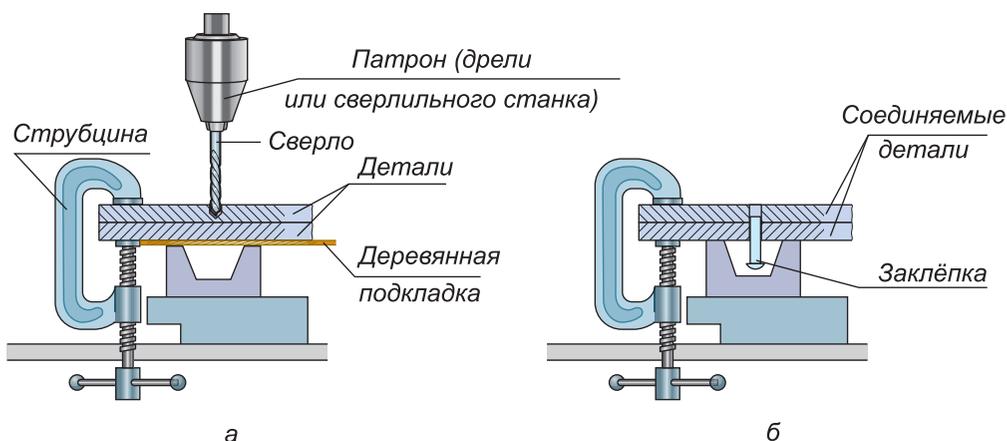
Соединение деталей заклёпками: а – сверление отверстия; б – приём вставки заклёпки
